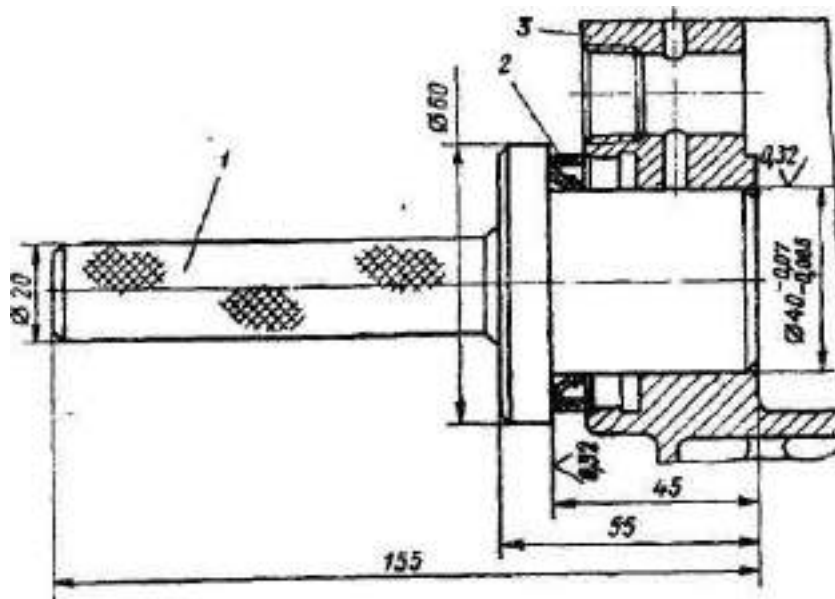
Знімач мастиловідбивного ковпачка клапана:
